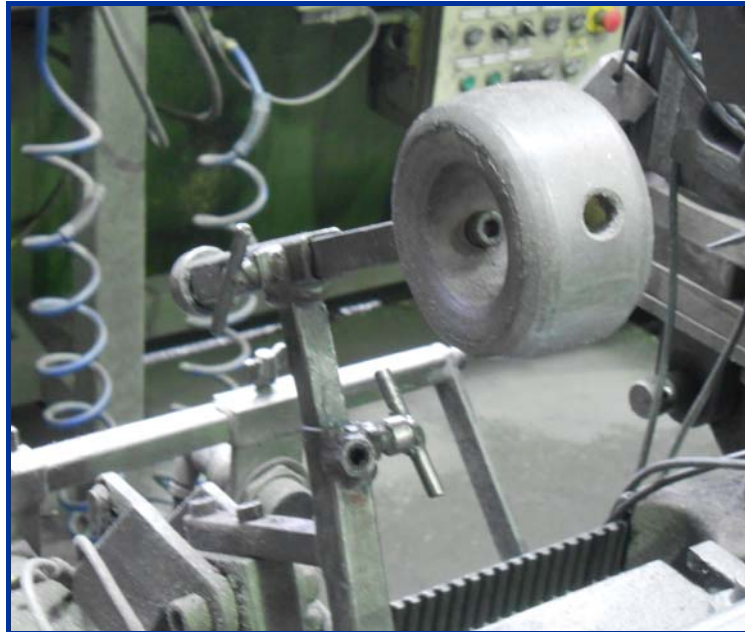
Detalle de los anclajes del cilindro de sujeción.
